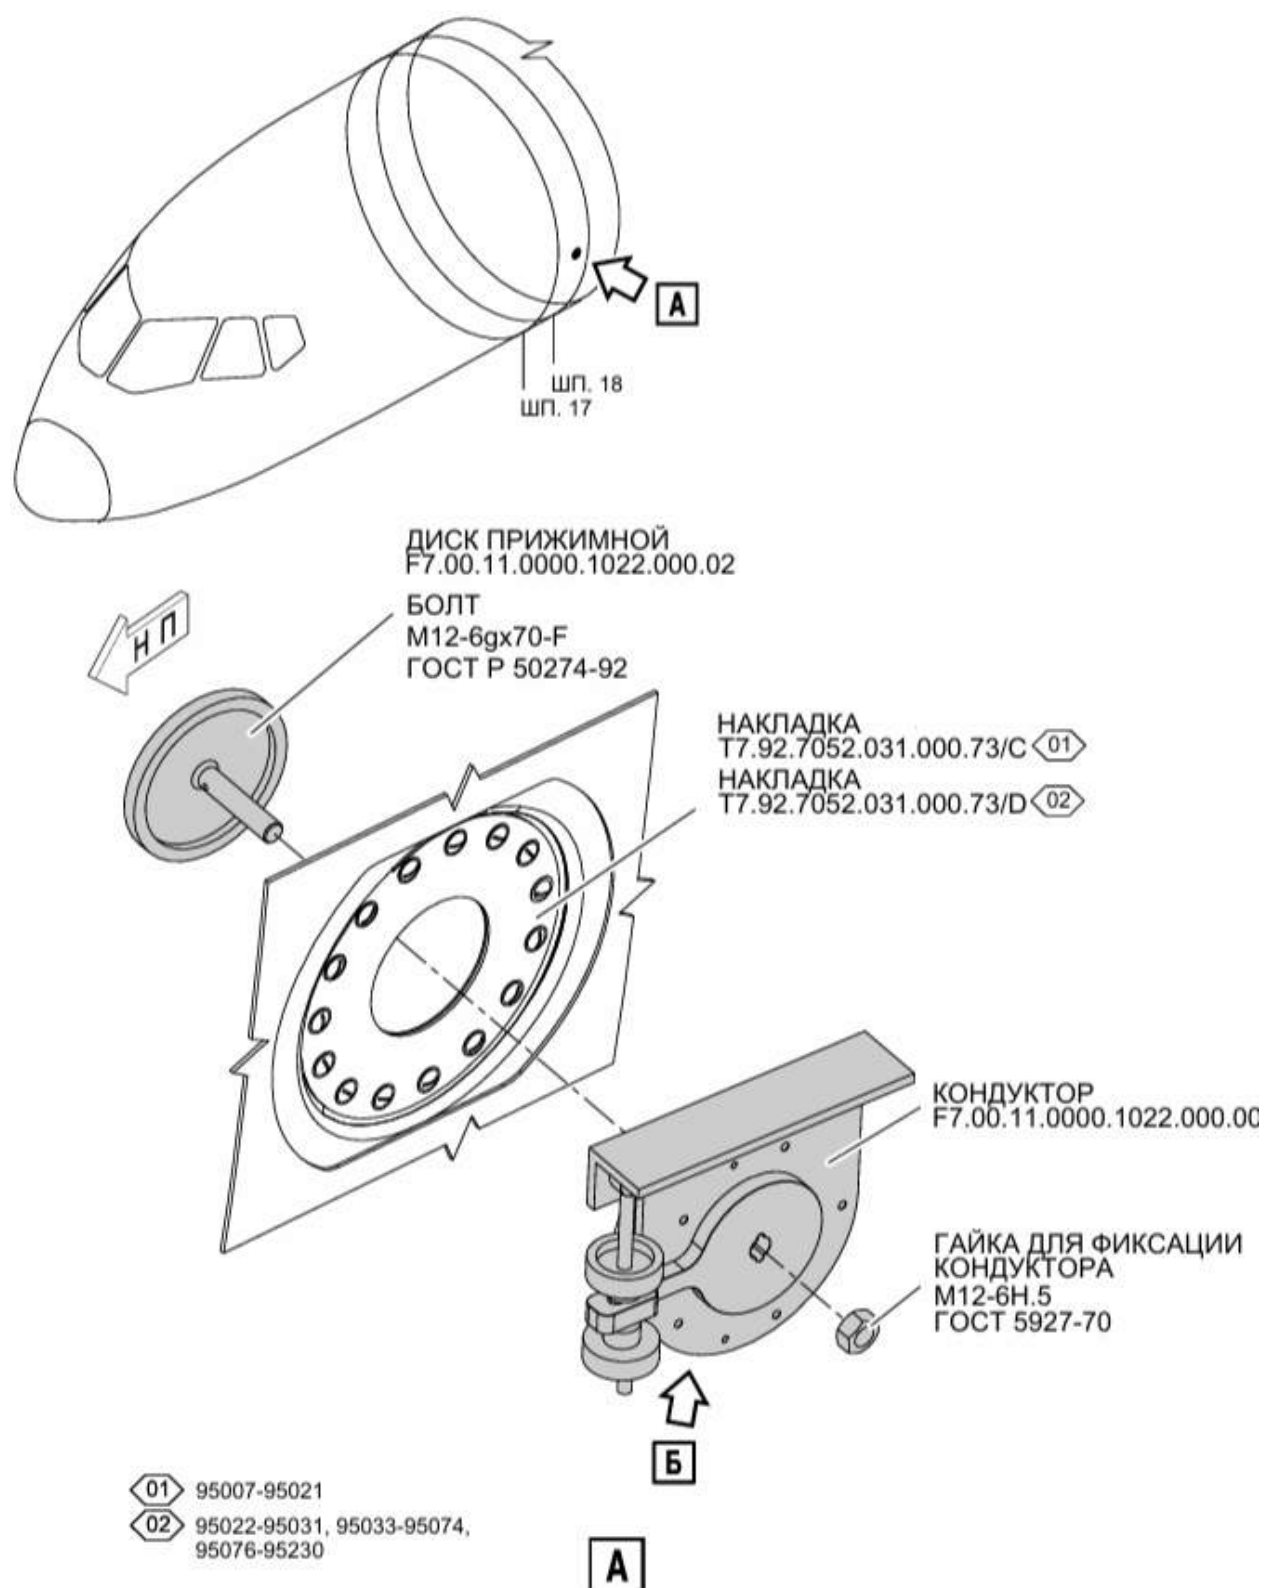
Установка кондуктора для выполнения отверстий крепления ДУА
